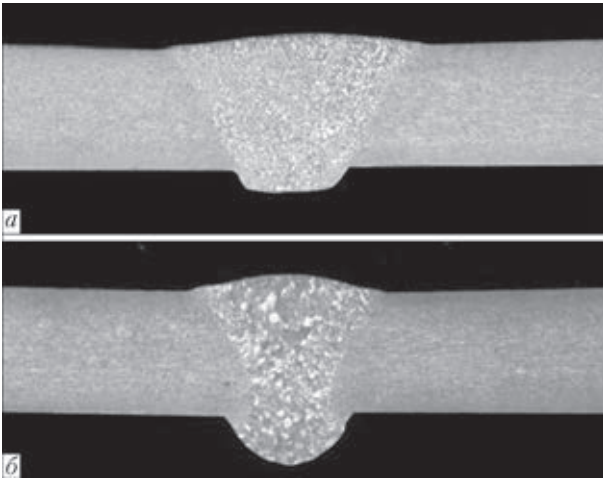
Макрошлиф сварного соединения из сплава 1420 (Al-Li-Mg) толщиной 6 мм, сваренного плазменно-дуговой сваркой в нижнем положении на подкладке с формирующей канавкой (а) и в режиме сквозного проплавления плазменной струи «keyhole» (б)
